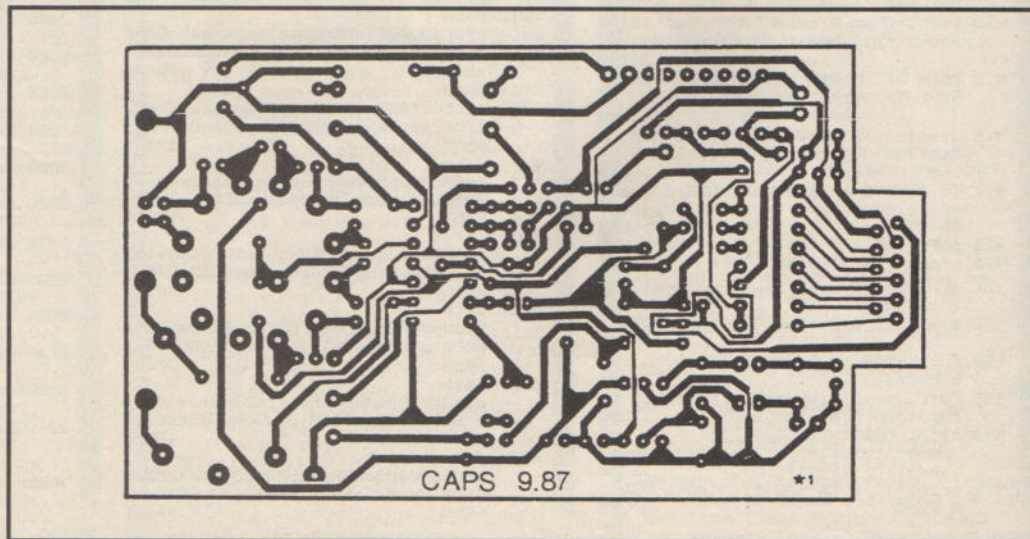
Platinenlayout zur Schaltung im Maßstab 1:1
